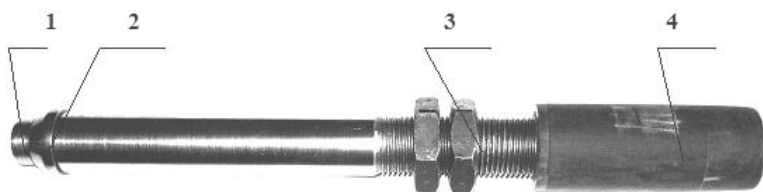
Инструментальная державка со сменным дорном: 1 - фиксирующая гайка; 2 – дорн; 3 – гайки для крепления токопроводящего кабеля; 4 – токоизоляционная втулка
